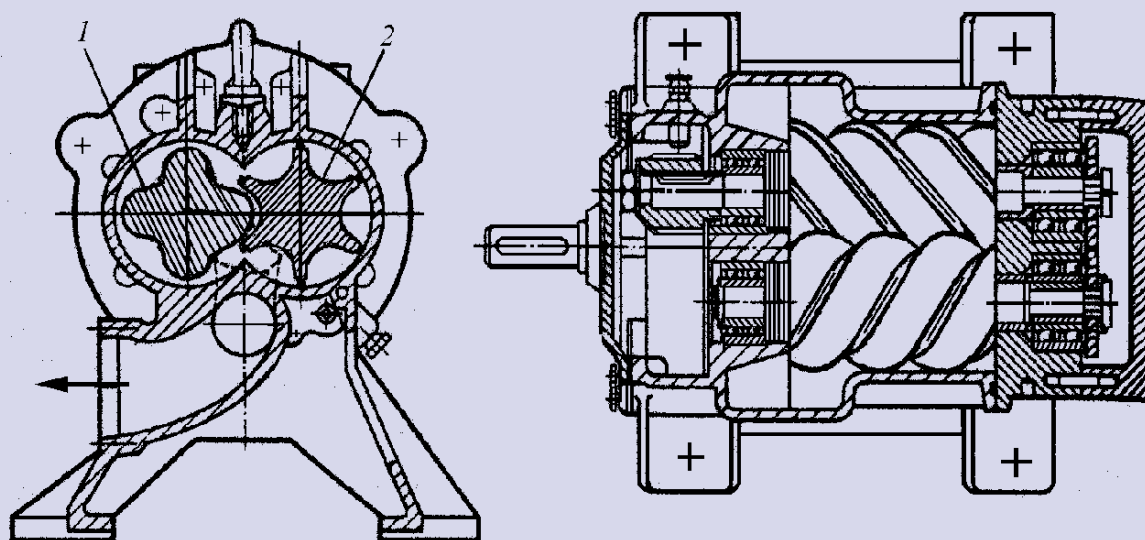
Конструктивная схема двухроторного винтового компрессора:
